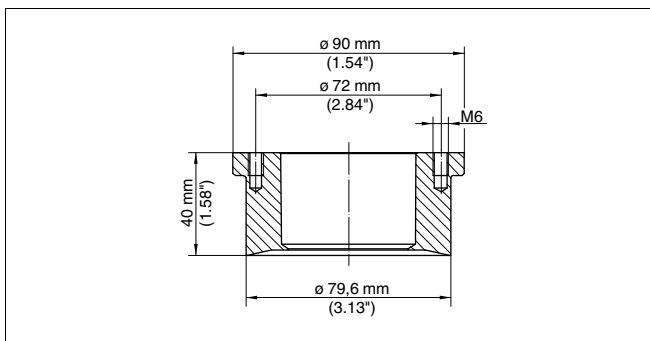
Размеры приварного штуцера LB для натяжного фланца
